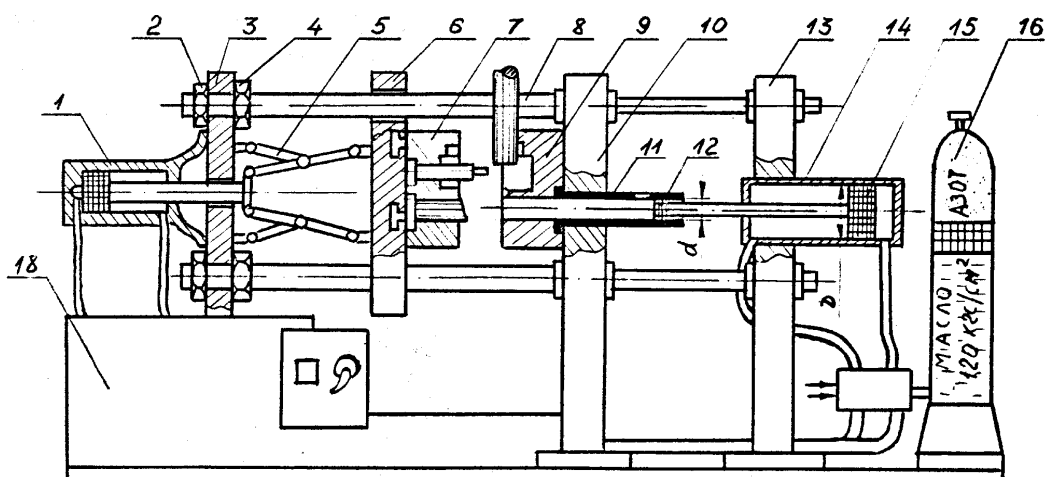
Схема машины литья под давлением с горизонтальной камерой прессования.
